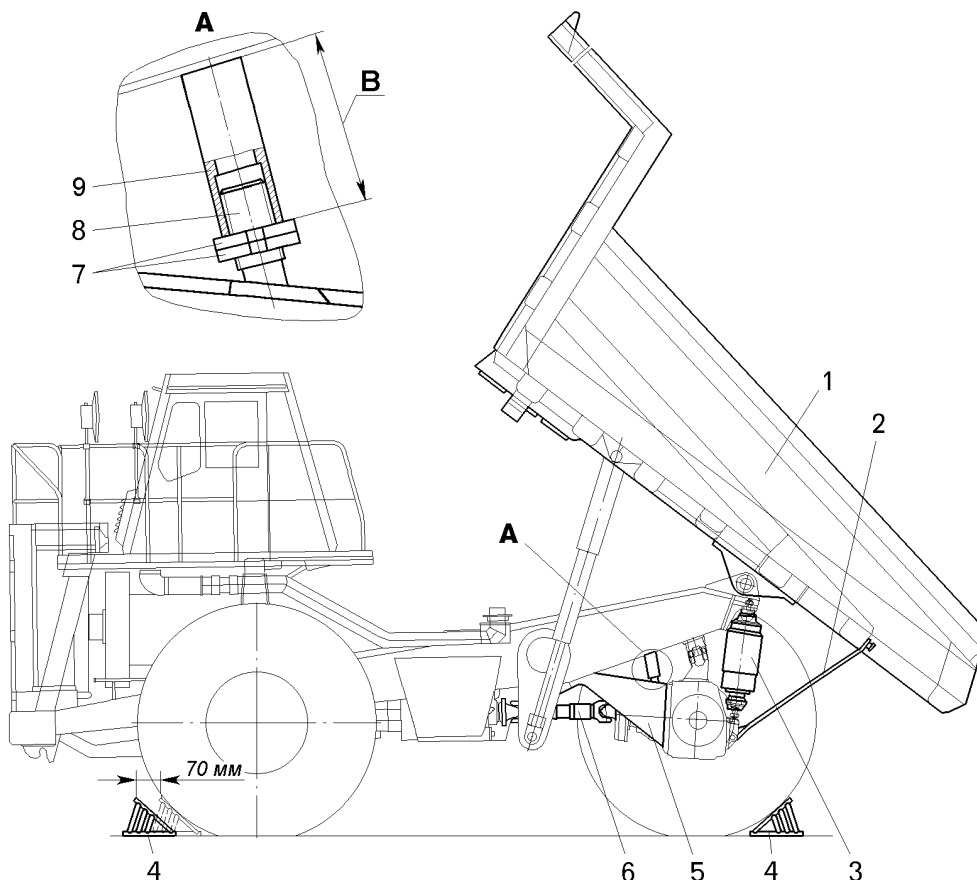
Разборка и сборка центрального шарнира задней подвески с поднятой платформой:
